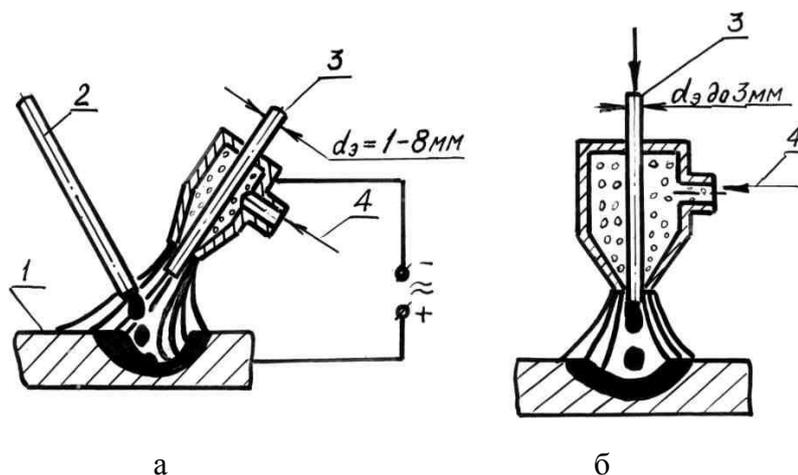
Дуговая сварка в среде защитного газа: а – неплавящимся; б – плавящимся электродами; 1- изделие; 2- присадочный пруток; 3- электрод; 4- горелка.
